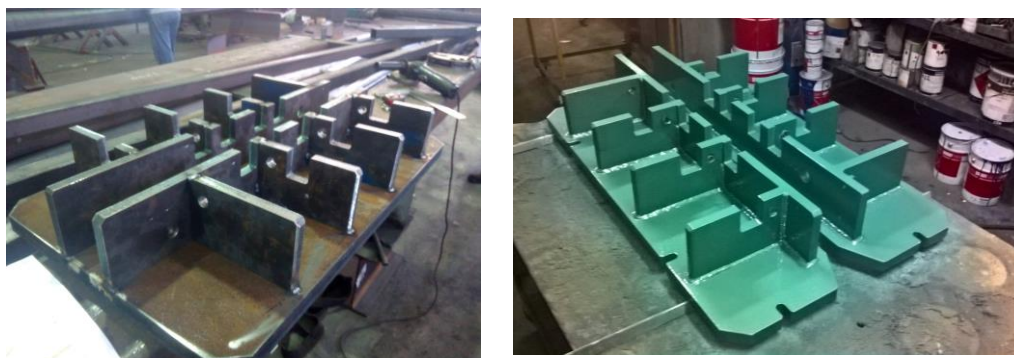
Imagens da peça após soldadura e após pintura
